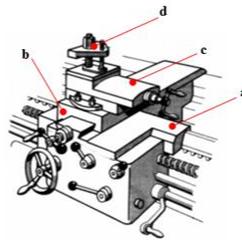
Elementos principais do carro ou carruagem, adaptado de (Gerling, 1967)
